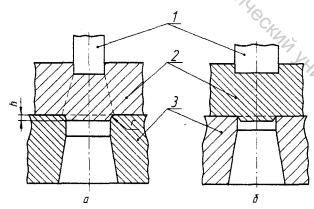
Схемы чистовой вырубки: а - на матрице со скругленными кромками; б - пуансоном больших размеров, чем матрица; 1 – пуансоны; 2 – материал заготовки; 3 - матрицы
